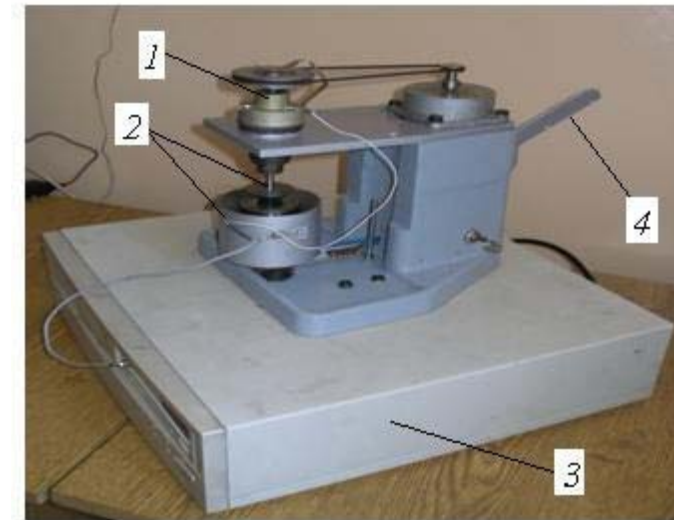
Внешний вид стенда для входного контроля подшипников качения: 1 – приводная установка; 2 – конические оправки для закрепления подшипника; 3 – измерительно-управляющий комплекс; 4 – рычаг нагружения
